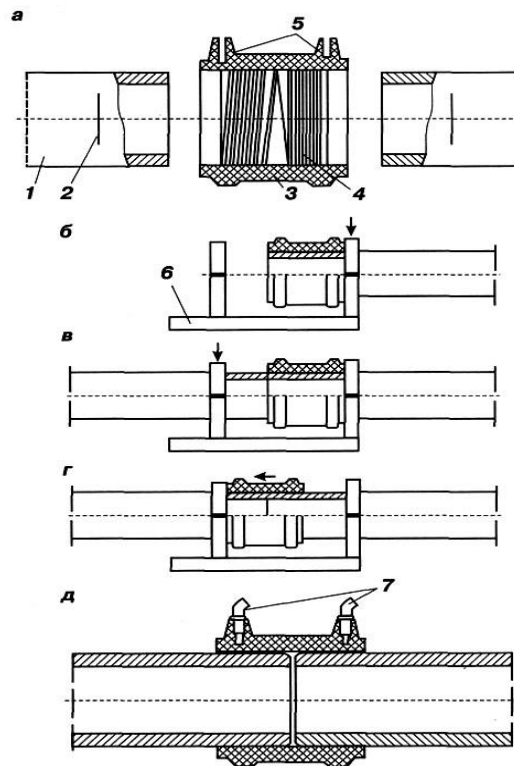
Соединение труб муфтой с закладным нагревателем: а – схема подготовки соединяемых элементов; б, в, г – схемы сборки стыка; д – собранный под сварку стык; 1 – труба; 2 – метка посадки муфты и механической обработки поверхности трубы; 3 – муфта; 4 – закладной нагреватель; 5 – клеммы токоподвода; 6 – приспособление для сборки; 7 – токоподводящие провода сварочного аппарата
